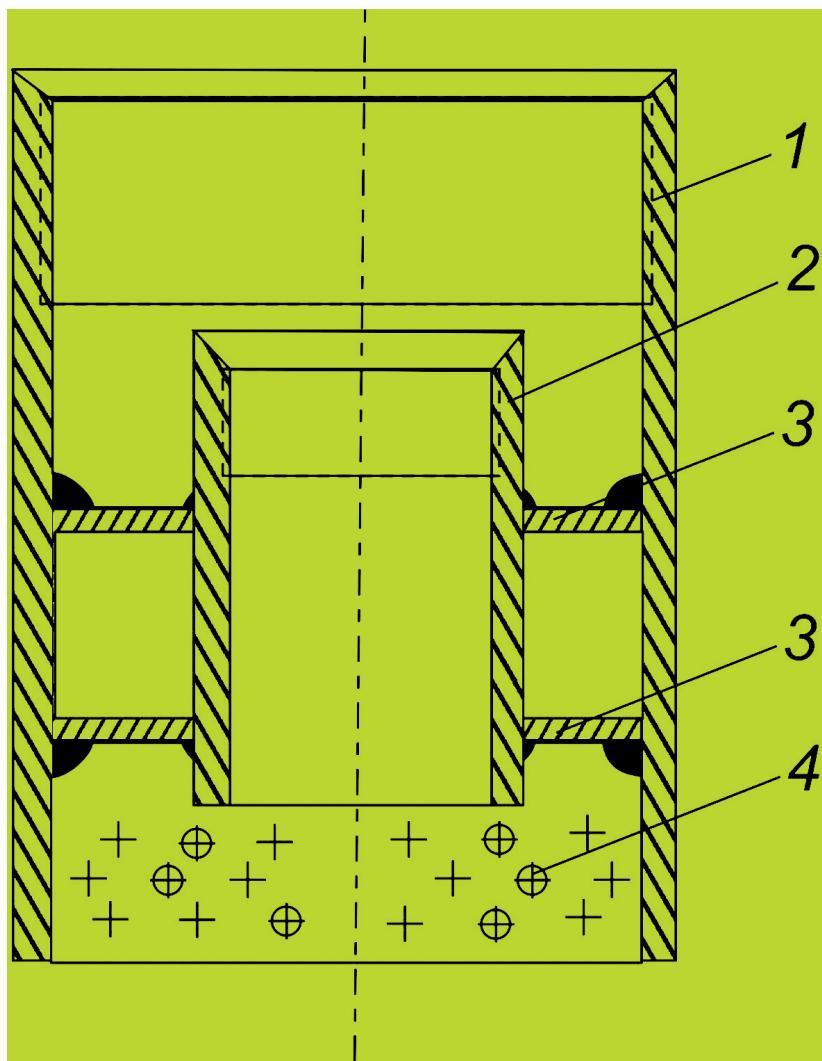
Промывочное устройство: 1 – корпус; 2 – замок; 3 – центрирующие шайбы; 4 – отверстия
